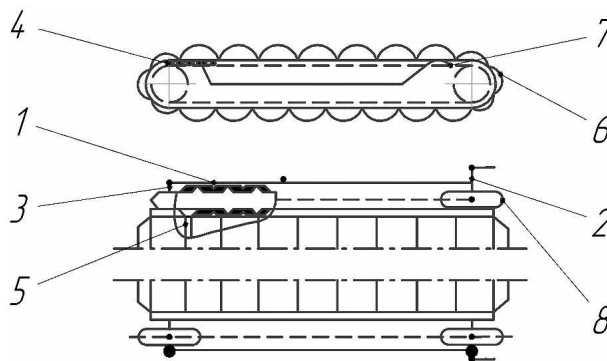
Схема улавливателя: 1 – рама; 2 – вал ведущий; 3 – вал ведомый; 4 – цепной контур; 5 – планка; 6 – амортизирующее полотно; 7 – короб; 8 – звездочка
